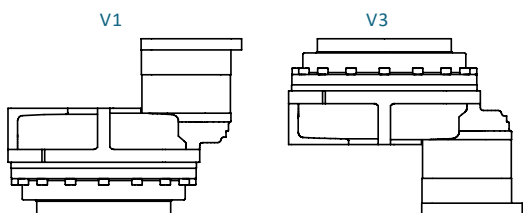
Einbaulagen - Antrieb vertikal, Eingangsposition wahlweise
